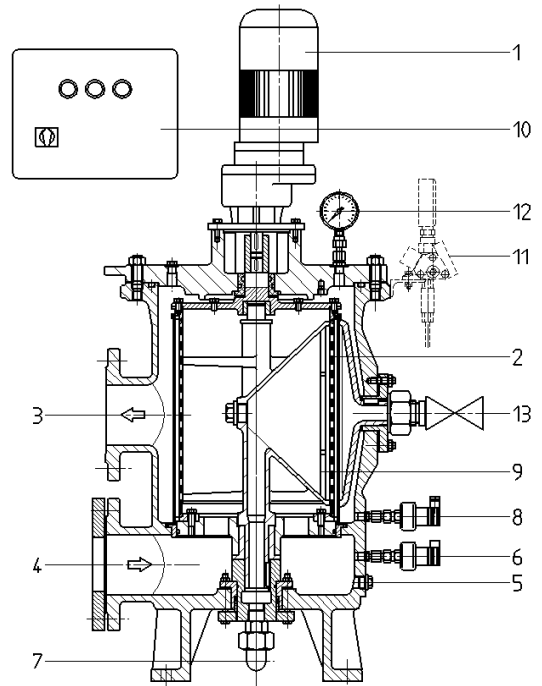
Bezeichnung der Hauptkomponenten R5-3
